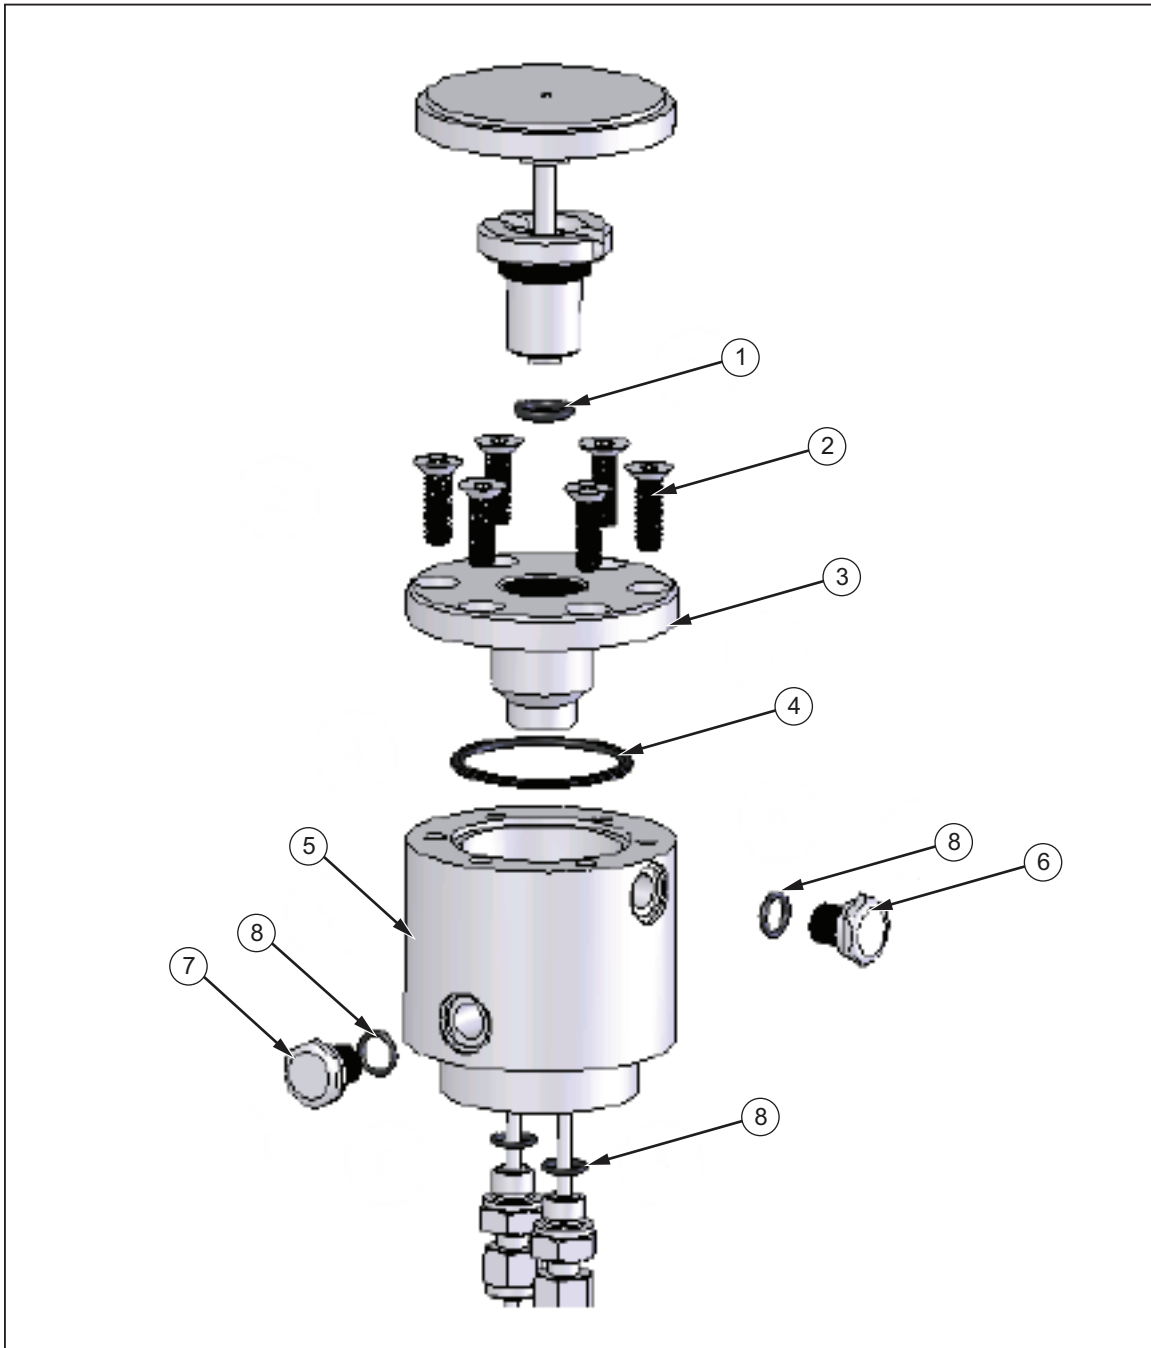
Сборочный чертеж корпуса поршневой пары - мм
